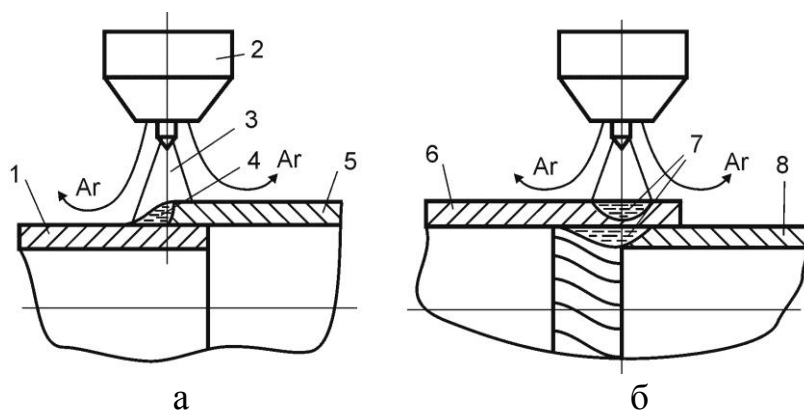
Две схемы аргонодуговой сваркопайки трубных заготовок из алюминия и титана: 1, 6 – труба из титана; 2 – сварочная горелка; 3 – дуга; 4, 7 – ванны жидкого металла; 5, 8 – труба из алюминия
